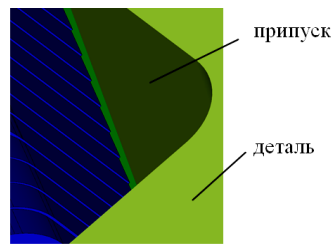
Аналіз припуску при чорновому фрезеруванні призматичного заглиблення
